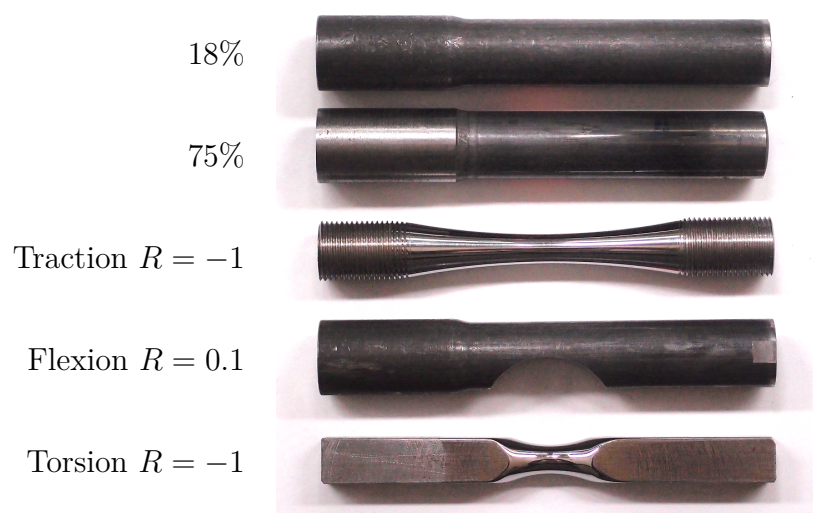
Eprouvettes extrudées brut de forge ainsi que des éprouvettes de fatigue.
